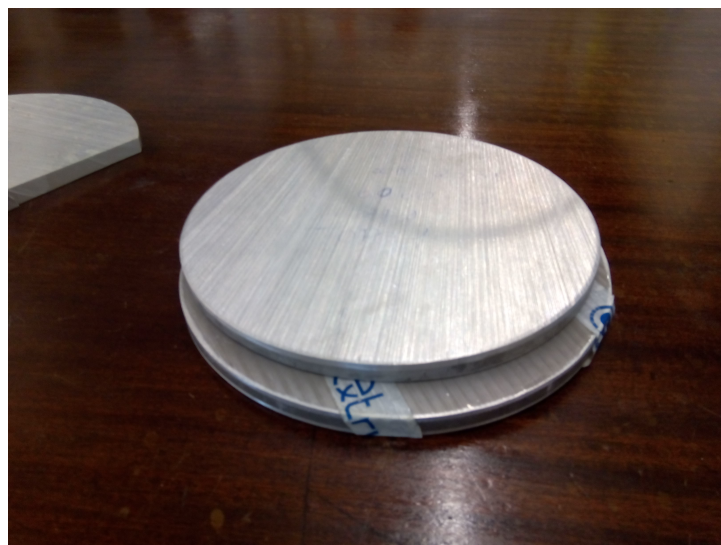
Bolachas serradas a partir de um bilete de alumínio.
